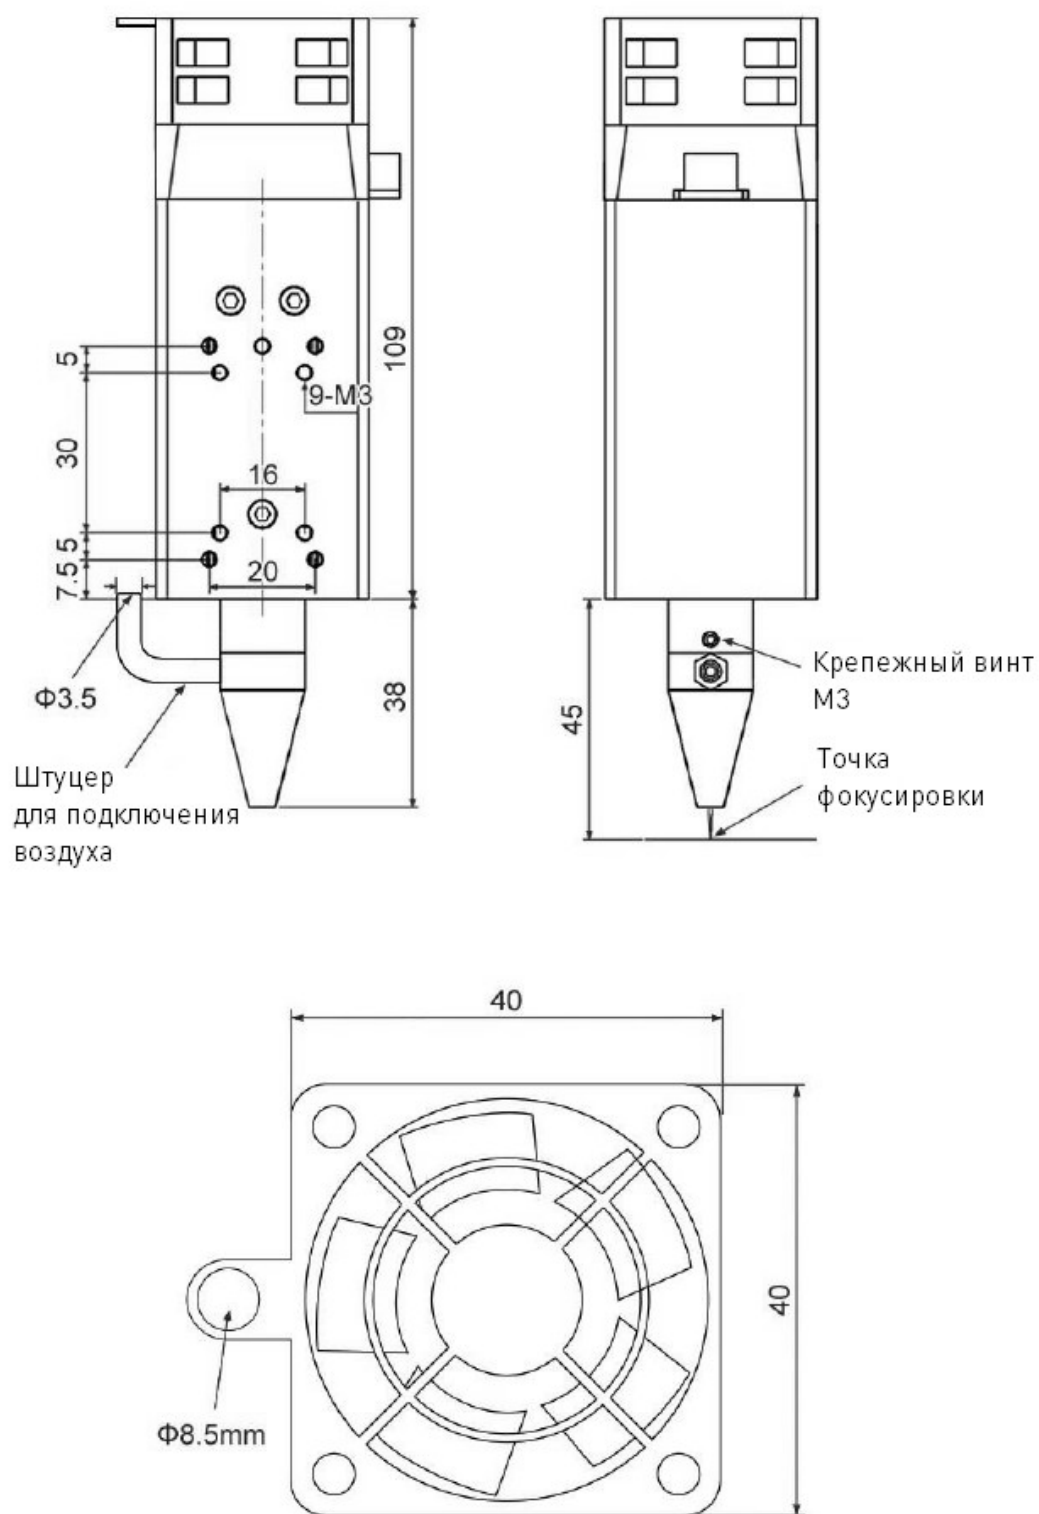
Габаритный чертеж лазерного модуля LT10W-12/24V.
